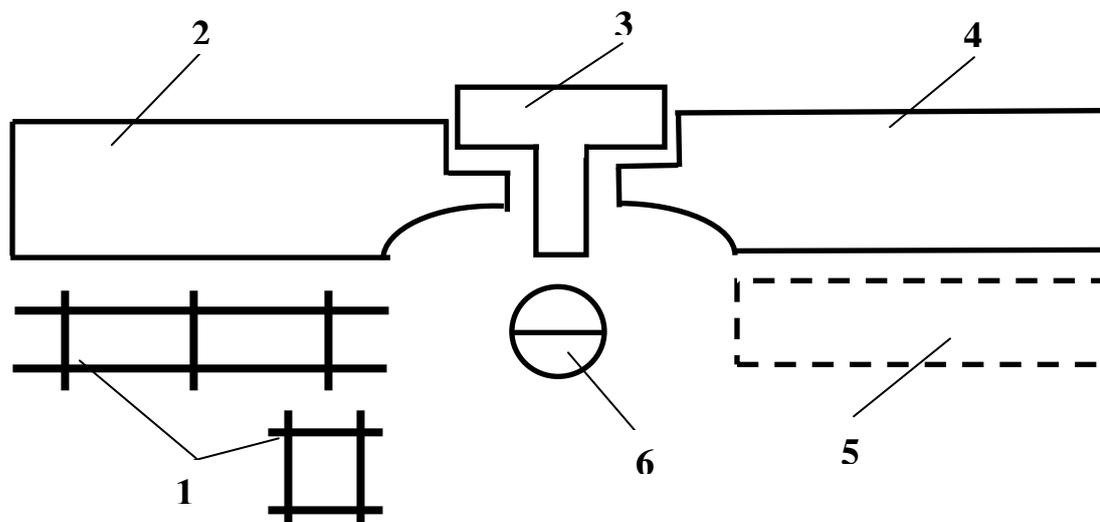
Схема организации рабочего места у односточной сварочной машины МТ-2023: 1 – связки (или контейнеры) с заготовленными продольными и поперечными стержнями плоского каркаса; 2 – стол для размещения заготовок; 3 – сварочная машина; 4 – приемный стол готового каркаса; 5 – площадка для размещения пакета (или контейнера) с партией готовых каркасов; 6 – рабочий-сварщик
